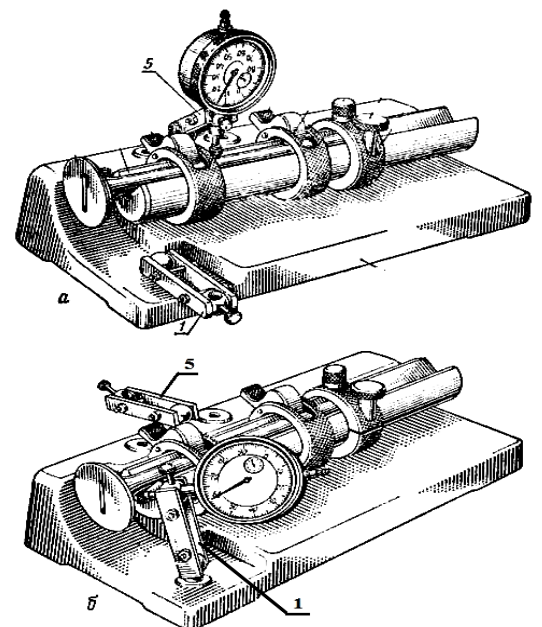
Приспособление для проверки биения стержня (а) и тарелки (б) клапана:
